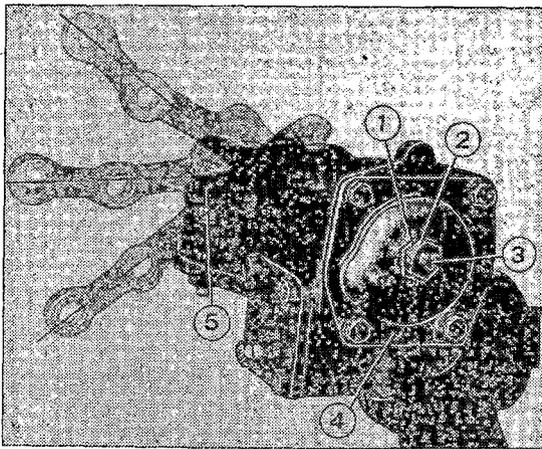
Рулевой механизм в сборе с сошкой:
